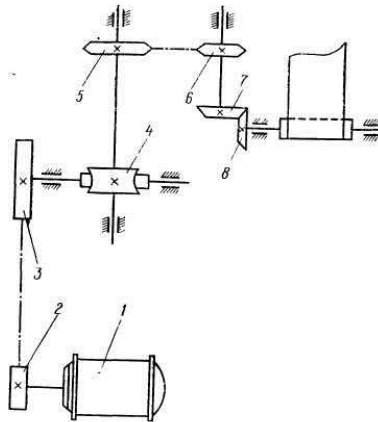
Схема приводу транспортера тістоподільної машини РМК: 1 – електродвигун; 2, 3 – клинопасова передача; 4 – черв'ячний редуктор; 5, 6 – ланцюгову передачу; 7, 8 – пара конічних коліс
